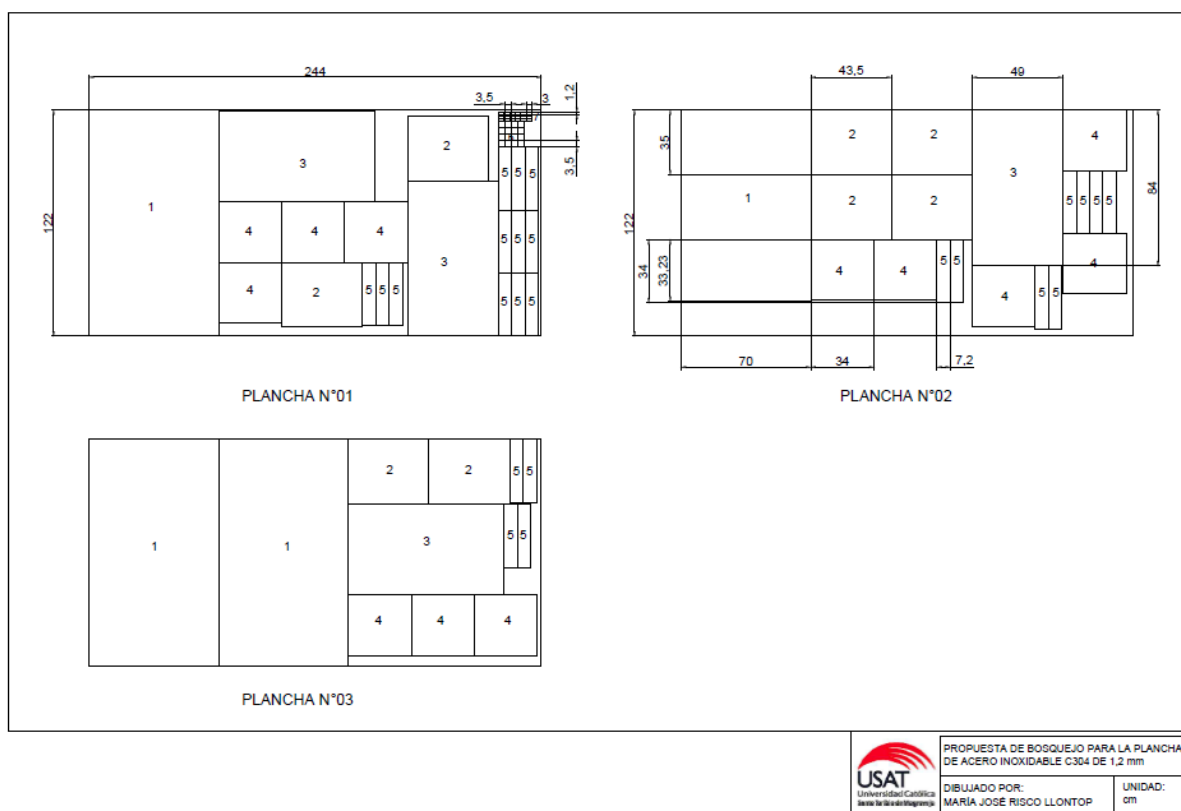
Propuesta de trazado de plancha de acero inoxidable C304 de 1,2 mm
